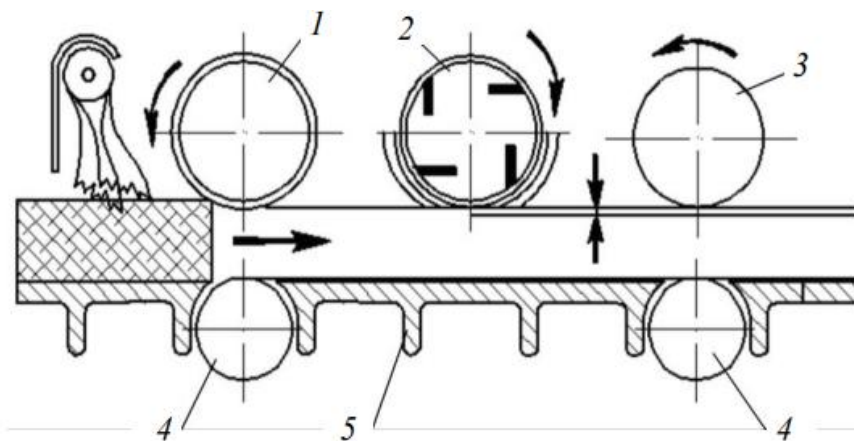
Схема влаштування рейсмусового верстата
